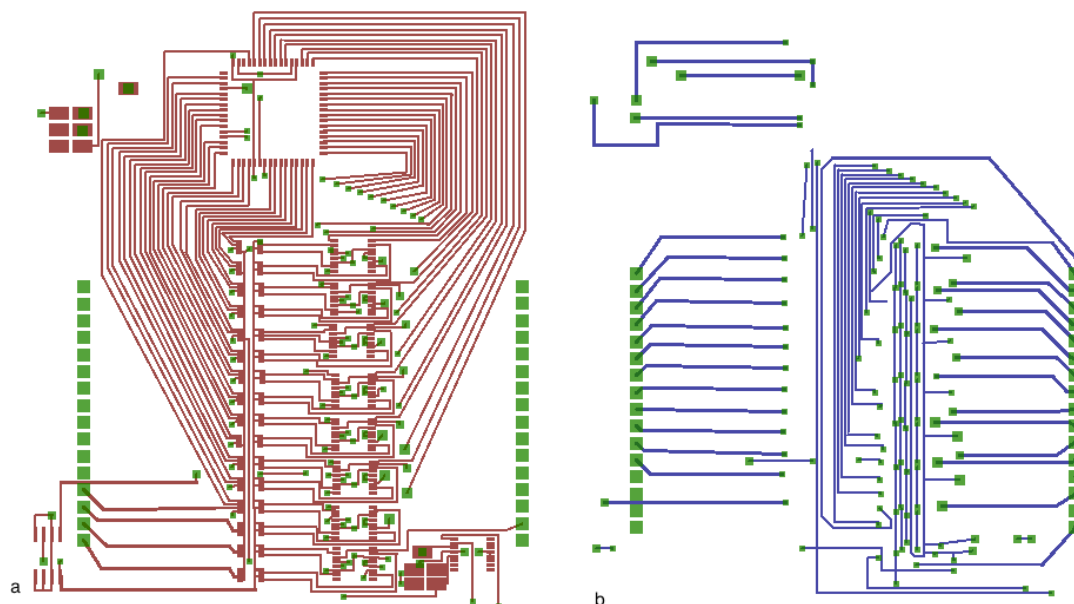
a) Camada superior e b) camada inferior da placa de PCB implementada.
